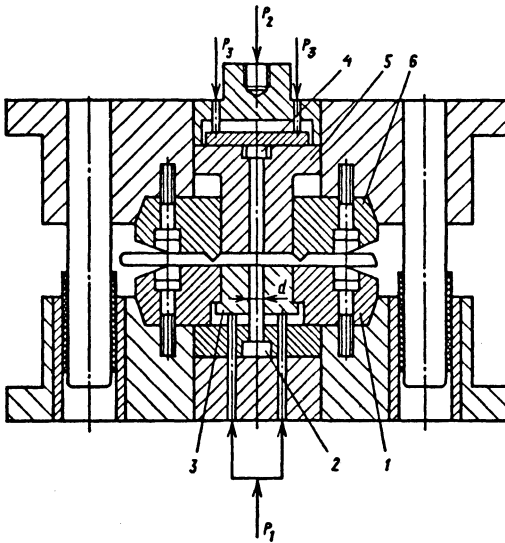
Конструкция штампа для чистовой вырубki-пробивки
